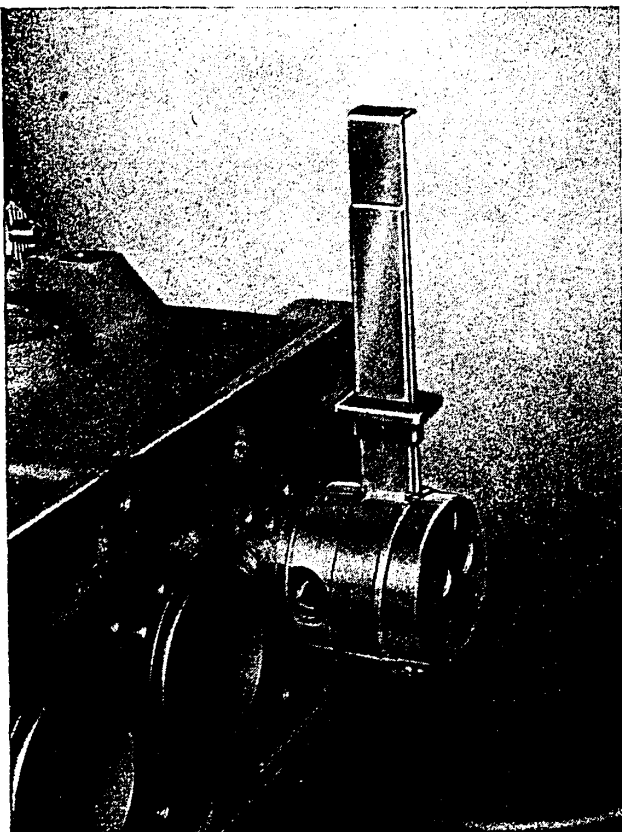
Kolben mit Klemmschelle (Werkzeug Nr. 324.018-M 99) in Zylinderlaufbuchse einsetzen
